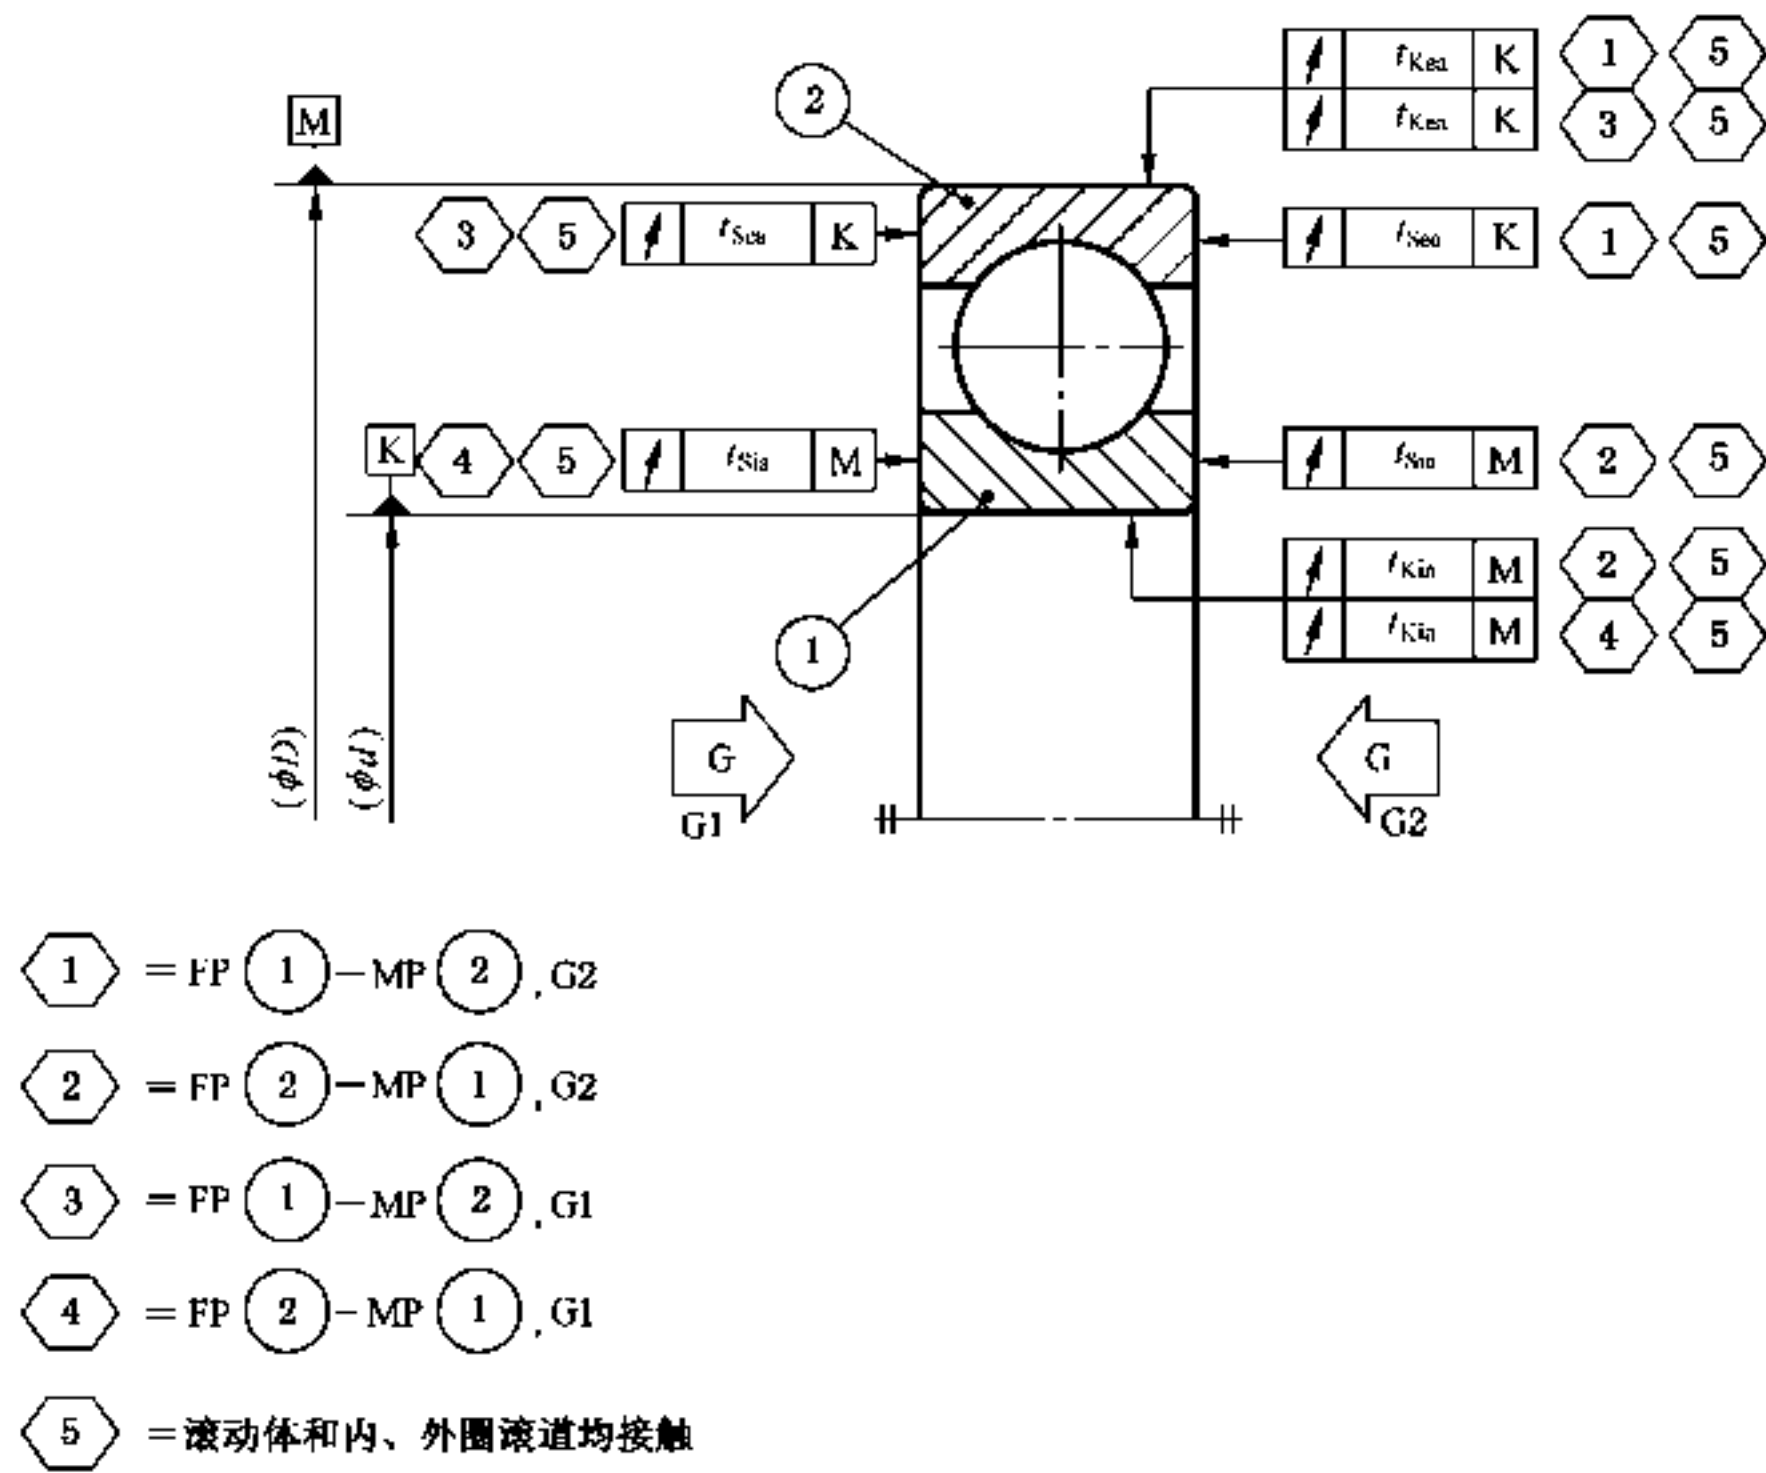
圆柱孔成套轴承的几何公差——深沟球轴承、双列深沟球轴承、双列角接触球轴承和四点接触球轴承
